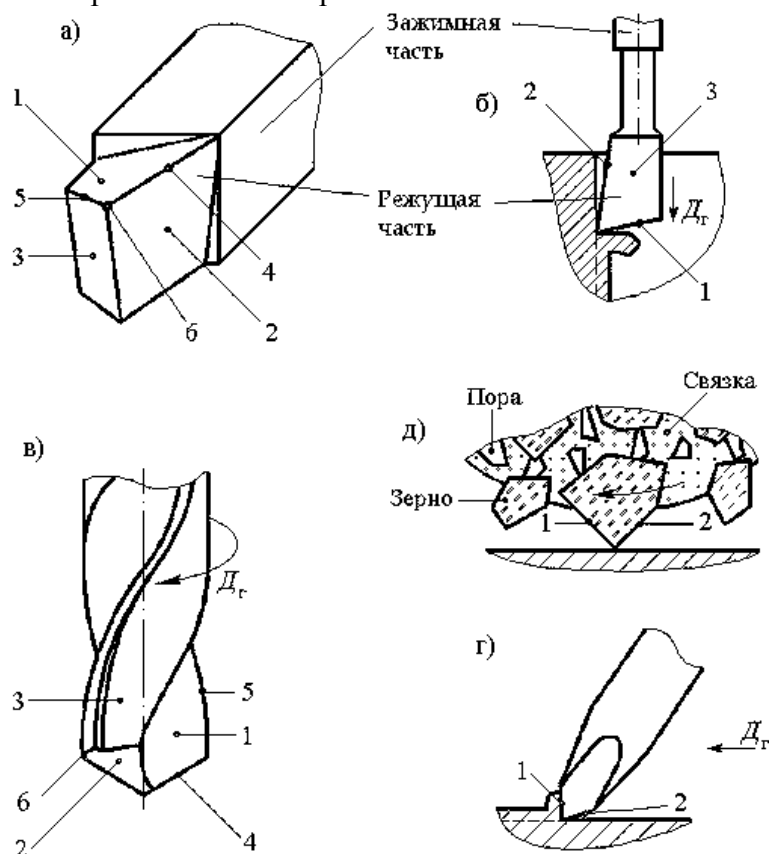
Составные части и рабочие поверхности инструментов:
